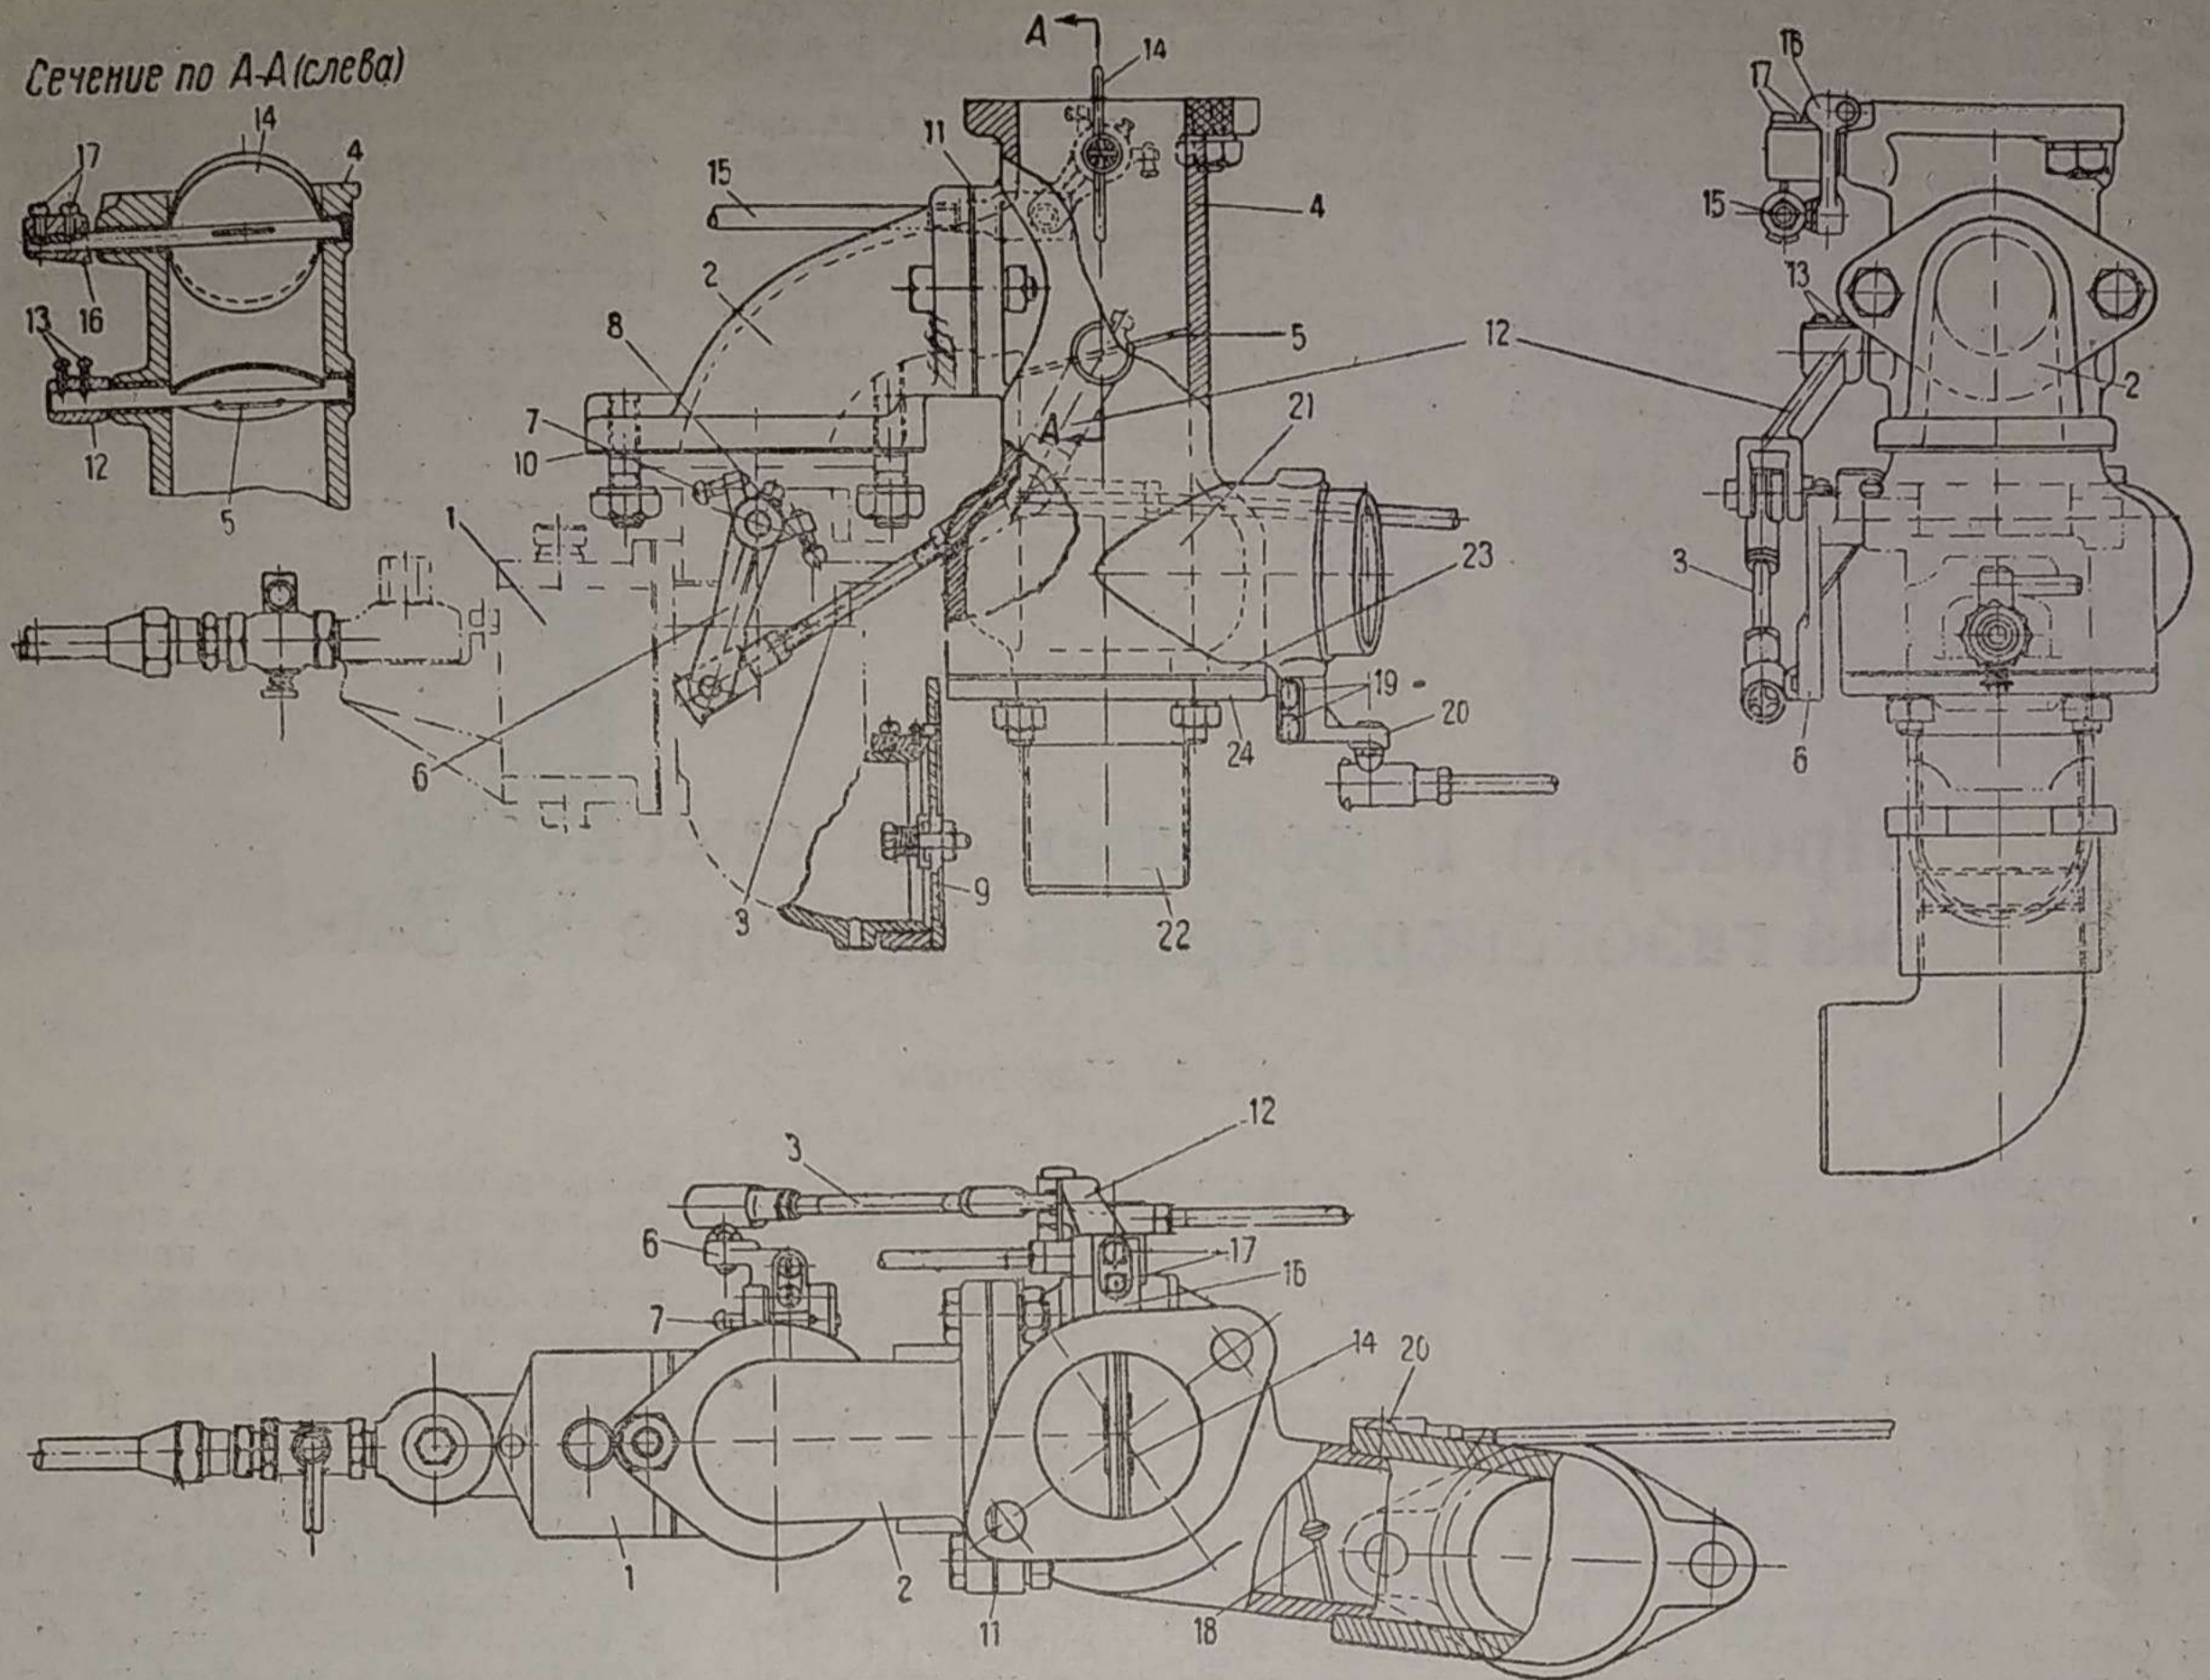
Смеситель двигателя трактора „сталинец-60“
